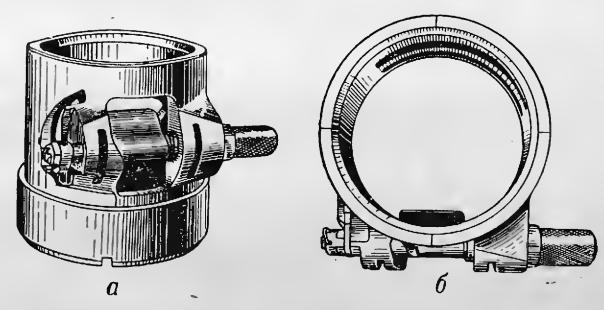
Предохранитель в положении «Закрыто»: a - вид сзади; 6 - вид сверху
